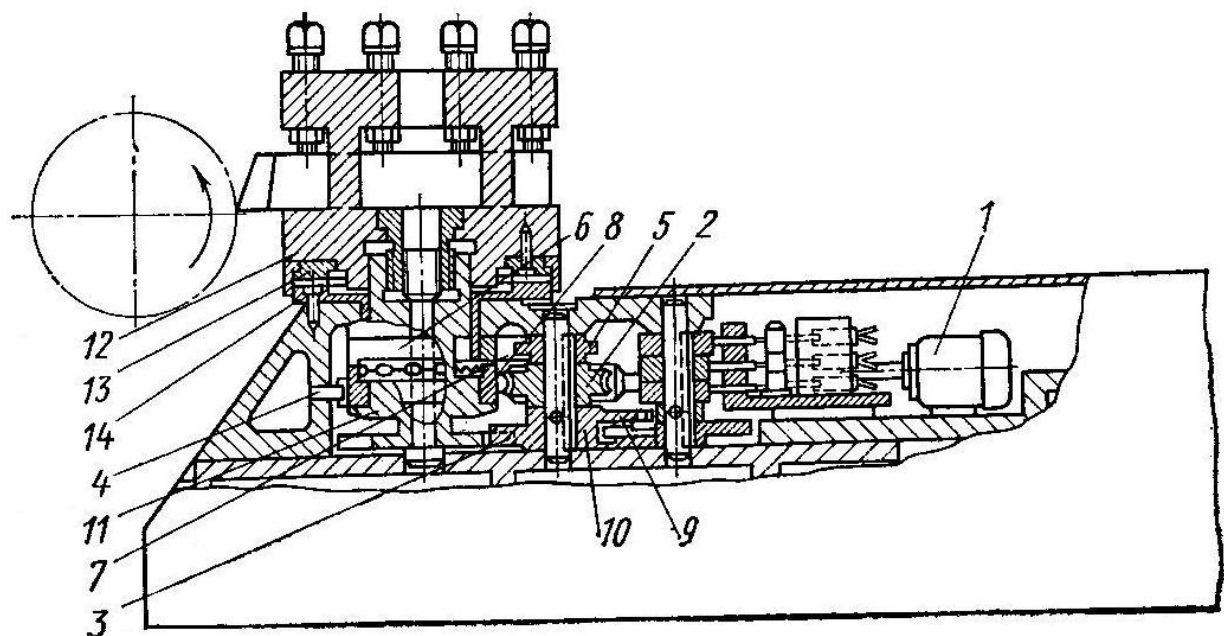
Різцева головка горизонтального супорта з механічним приводом для повороту
